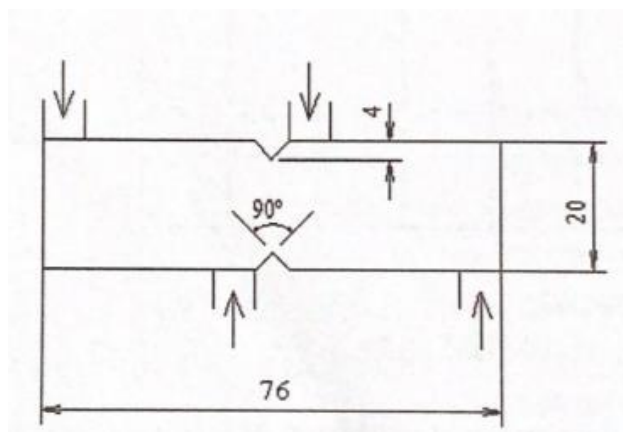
Carregamentos, geometria e dimensões (em mm) do provete para o ensaio de corte [2].
